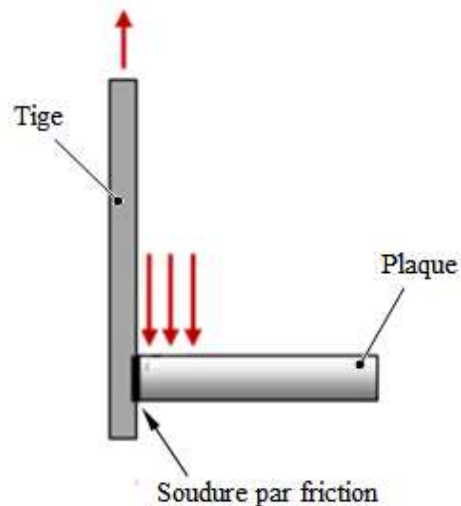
Assemblages (tige - plaque) soudés par friction
